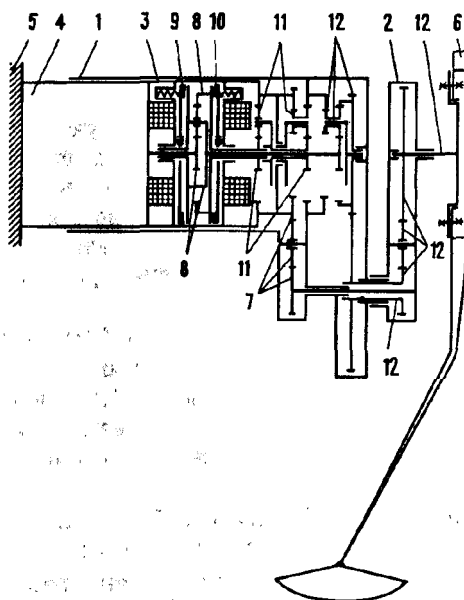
Кинематическая схема колесо-шагающего механизма с частичной блокировкой:
